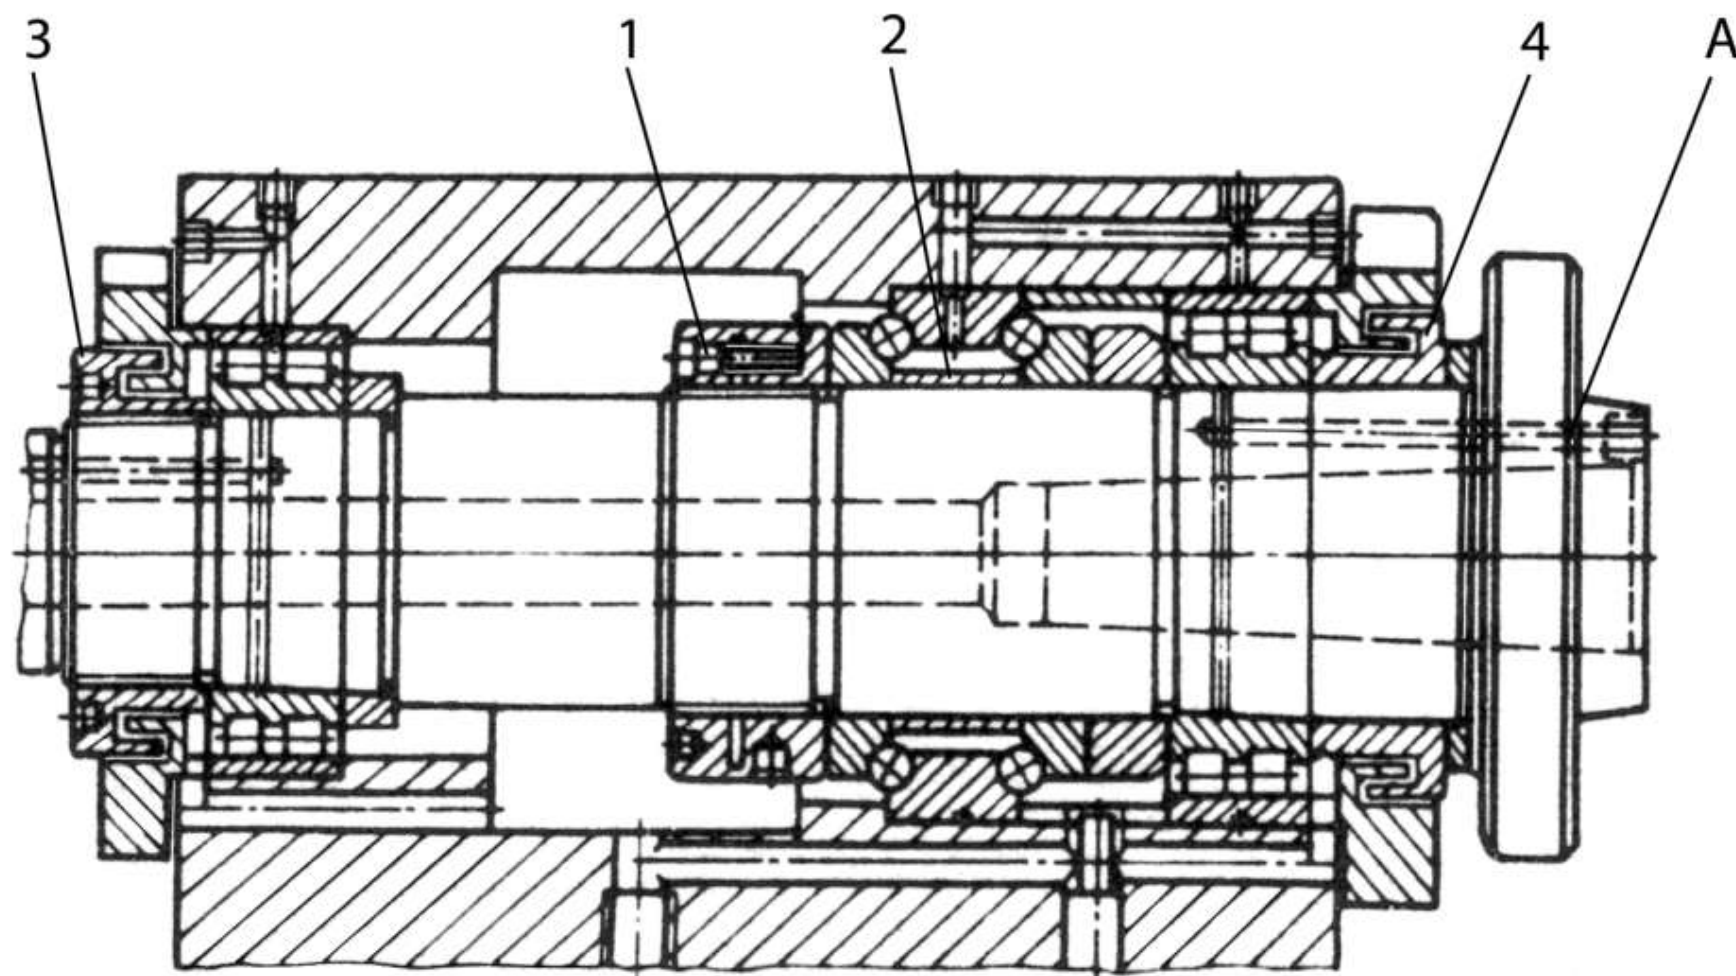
Шпиндельный узел с двухрядным роликовым подшипником типа 3182100К и упорно-радиальным шариковым подшипником типа 178800:
